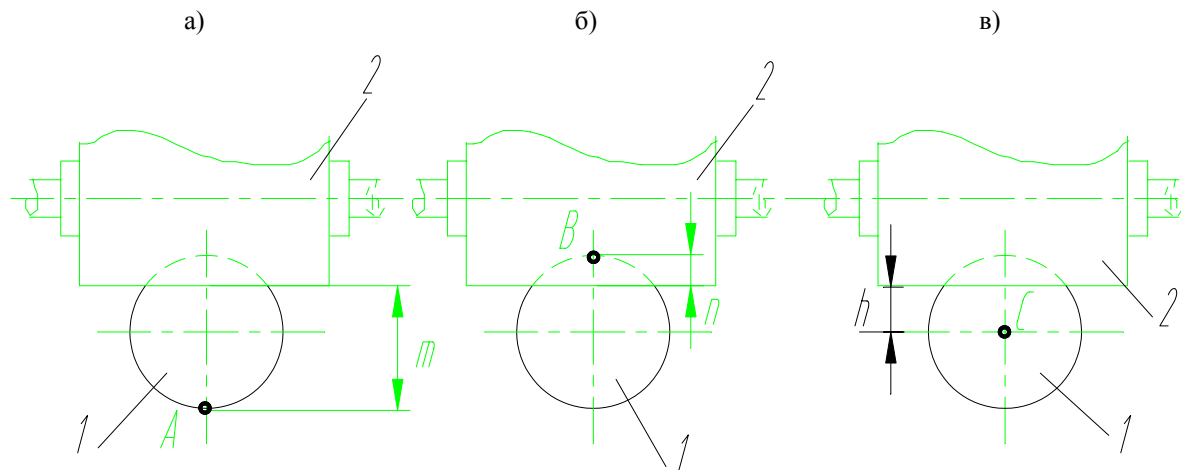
Фрезерование лыски на вале (1 - заготовка вала; 2 - фреза).
